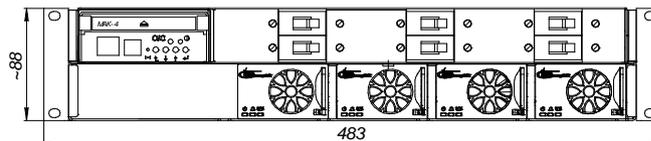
Габаритный чертеж УЭПС-7К 48/148 (60/120)-44-1
